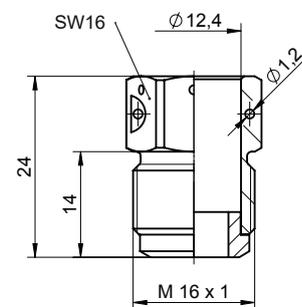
Montageadapter M16x1, Typ 6419A21D für Sensor mit 7/16" Buchse
